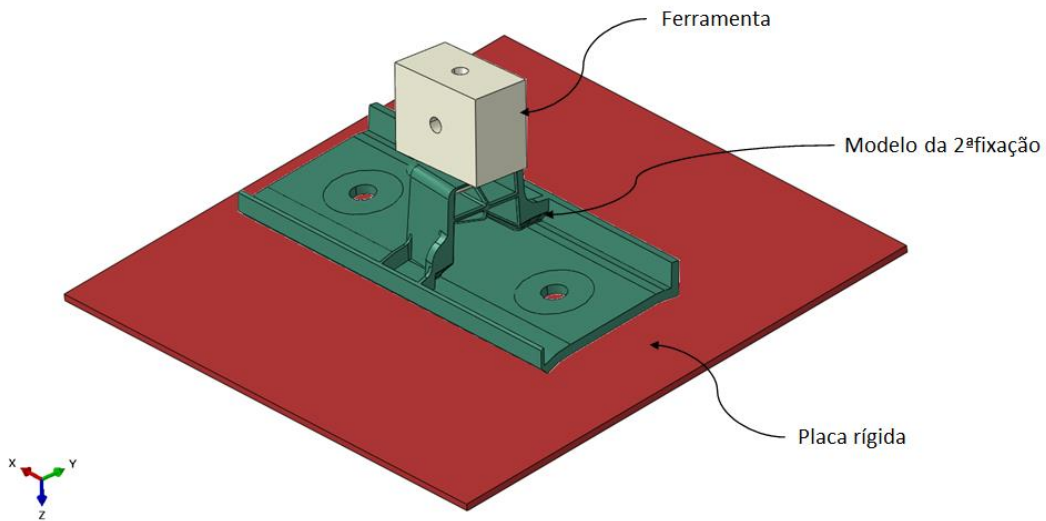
Montagem do conjunto da 2ª fixação no módulo "Assembly" do Abaqus.
